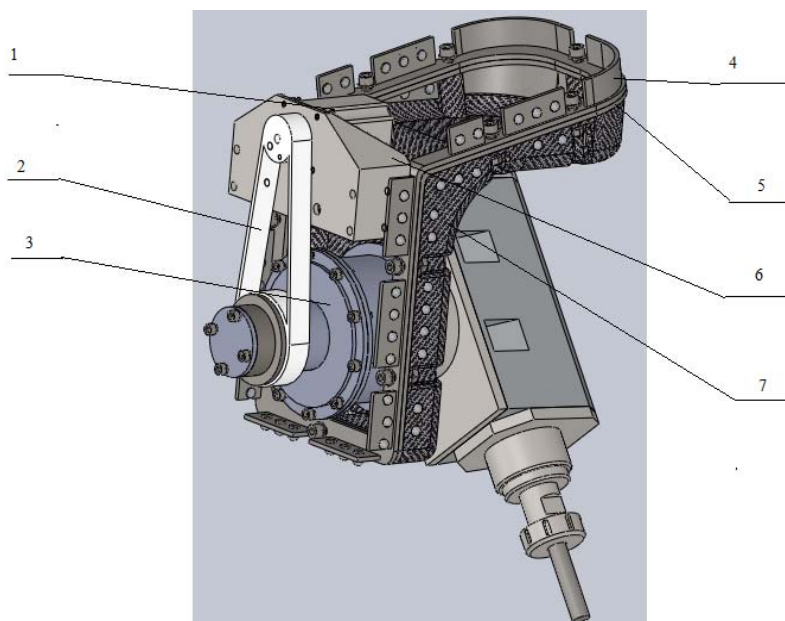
Трехмерная модель привода поворота фрезерной головки:
